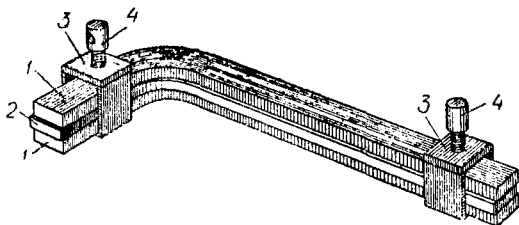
Копир для опиловки угольников станка для ножовочных полотен:
